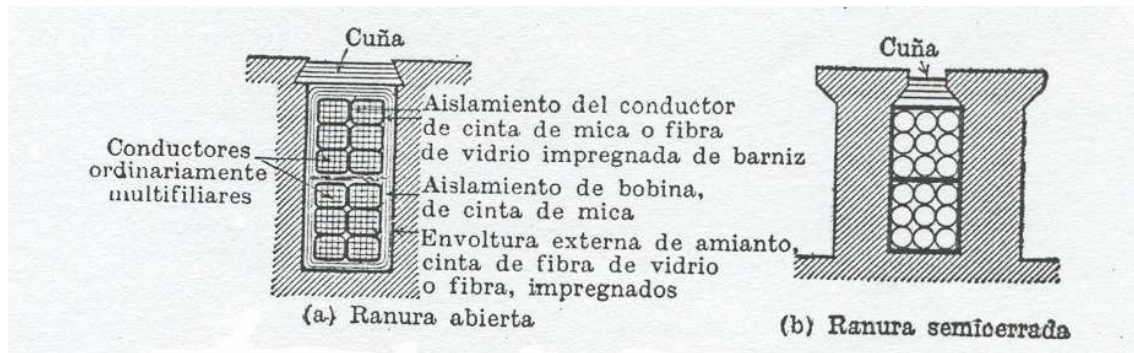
Sección transversal de ranuras típicas para alternadores.
